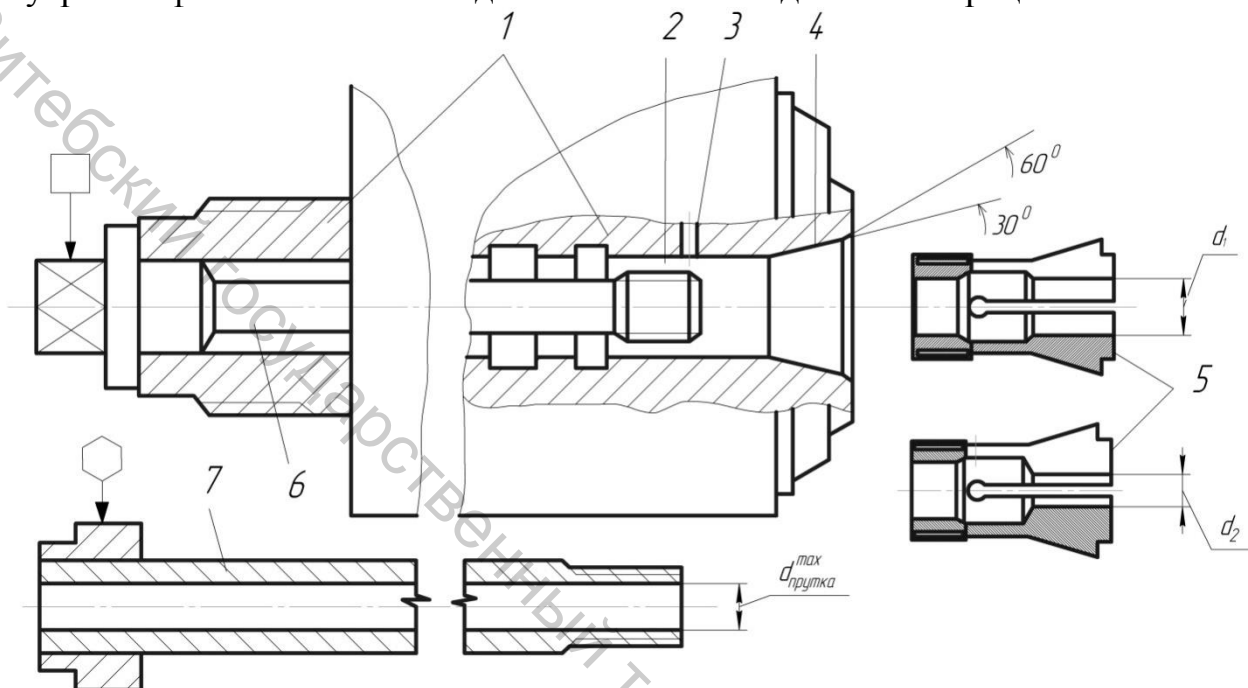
Шпиндель внутришлифовального станка с непосредственным базированием и зажимом заготовок в цанга
